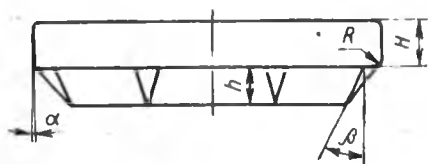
Заготовка дроссельного фланца к табл. 1.18
